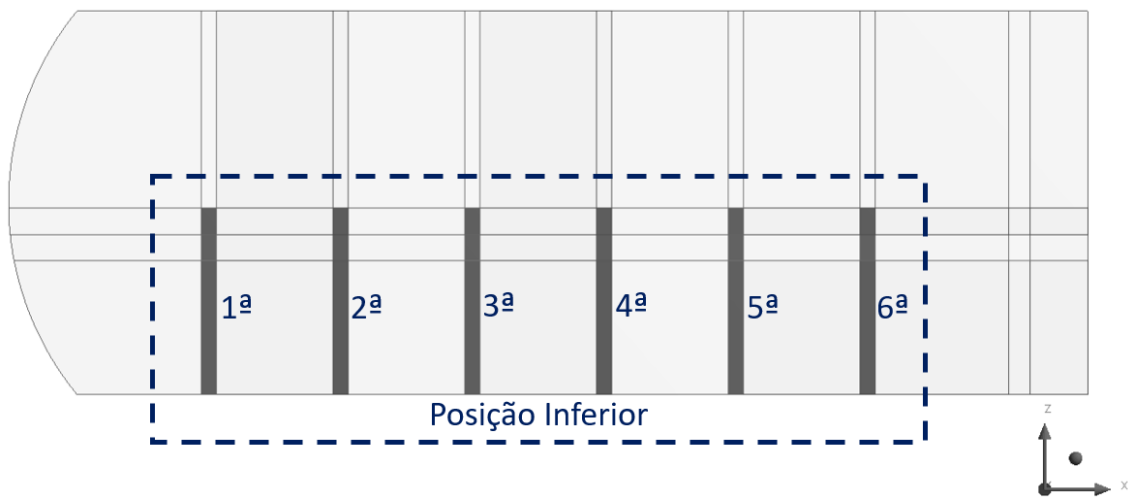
Posições testadas individualmente para o quebra-ondas posicionado na parte do inferior do equipamento
